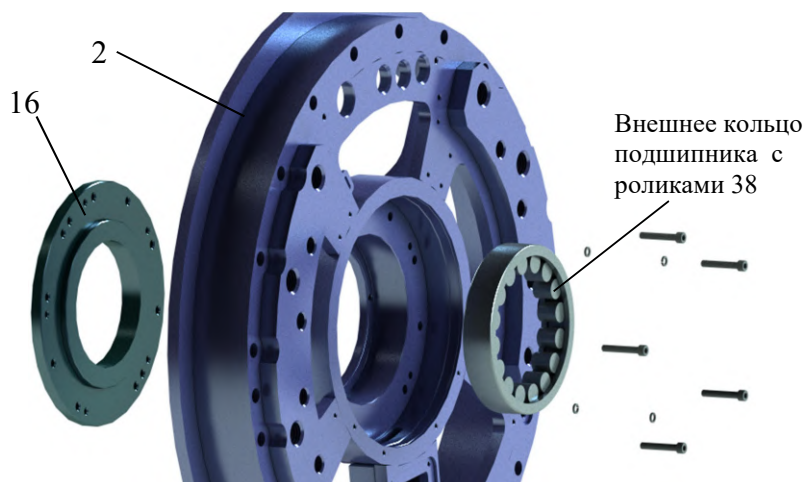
Демонтаж деталей из подшипникового щита (сторона тормоза)
